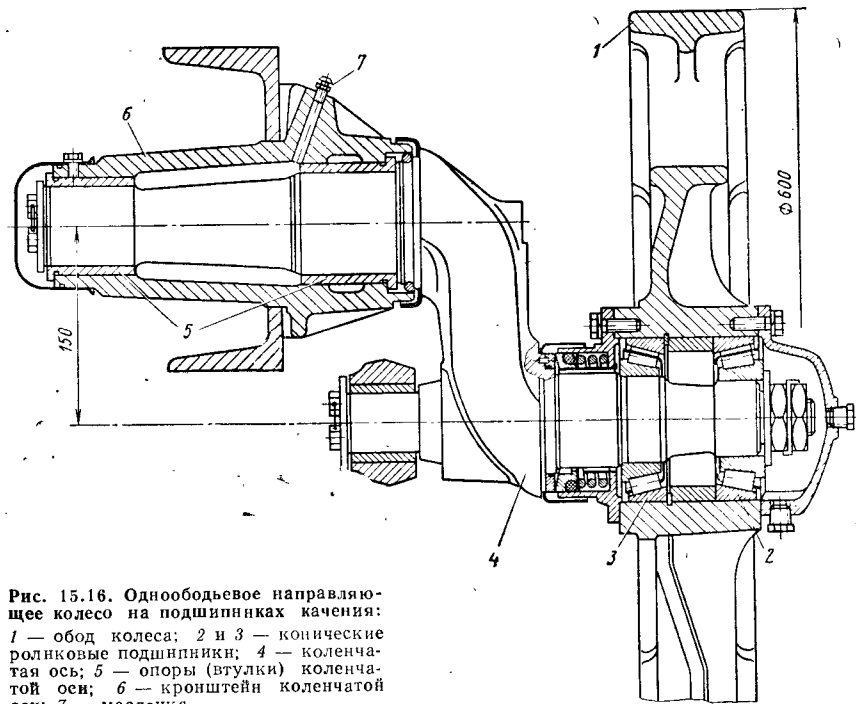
Одноободьево направляющее колесо на подшипниках качения: 1 — обод колеса; 2 и 3 — конические роликовые подшипники; 4 — коленчатая ось; 5 — опоры (втулки) коленчатой оси; 6 — кронштейн коленчатой оси; 7 — масленка
